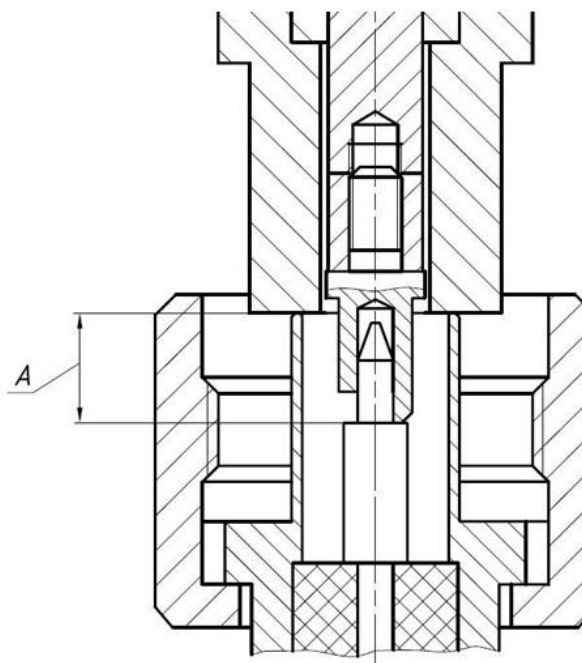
Проверка размера «А» соединителя «вилка»
